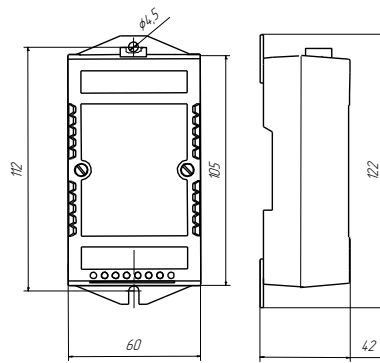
Габаритные и присоединительные размеры MC1206
